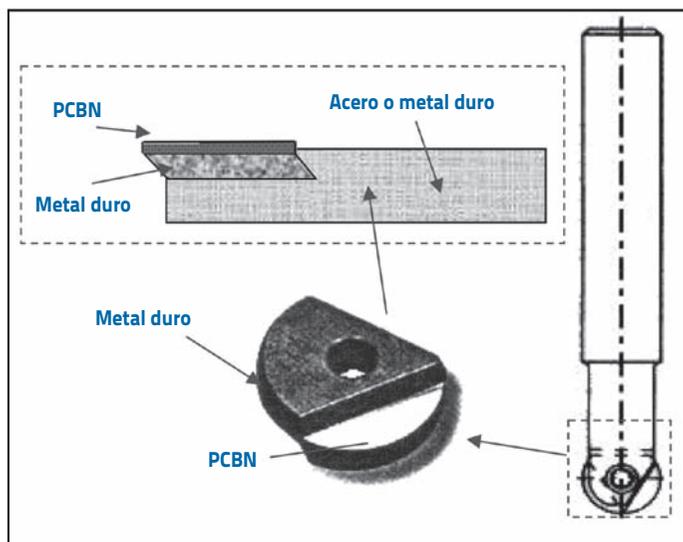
Estructura de una herramienta de PCBN, para una fresa esférica.
